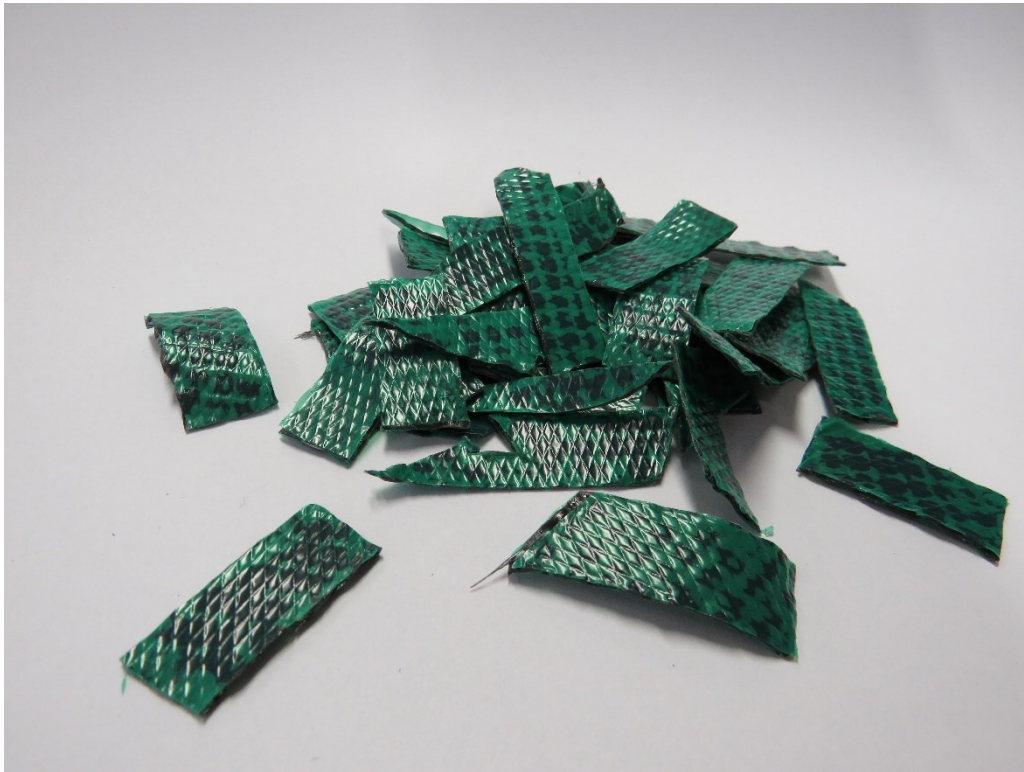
Chips di prepeg di dimensioni 10 x 50 mm
